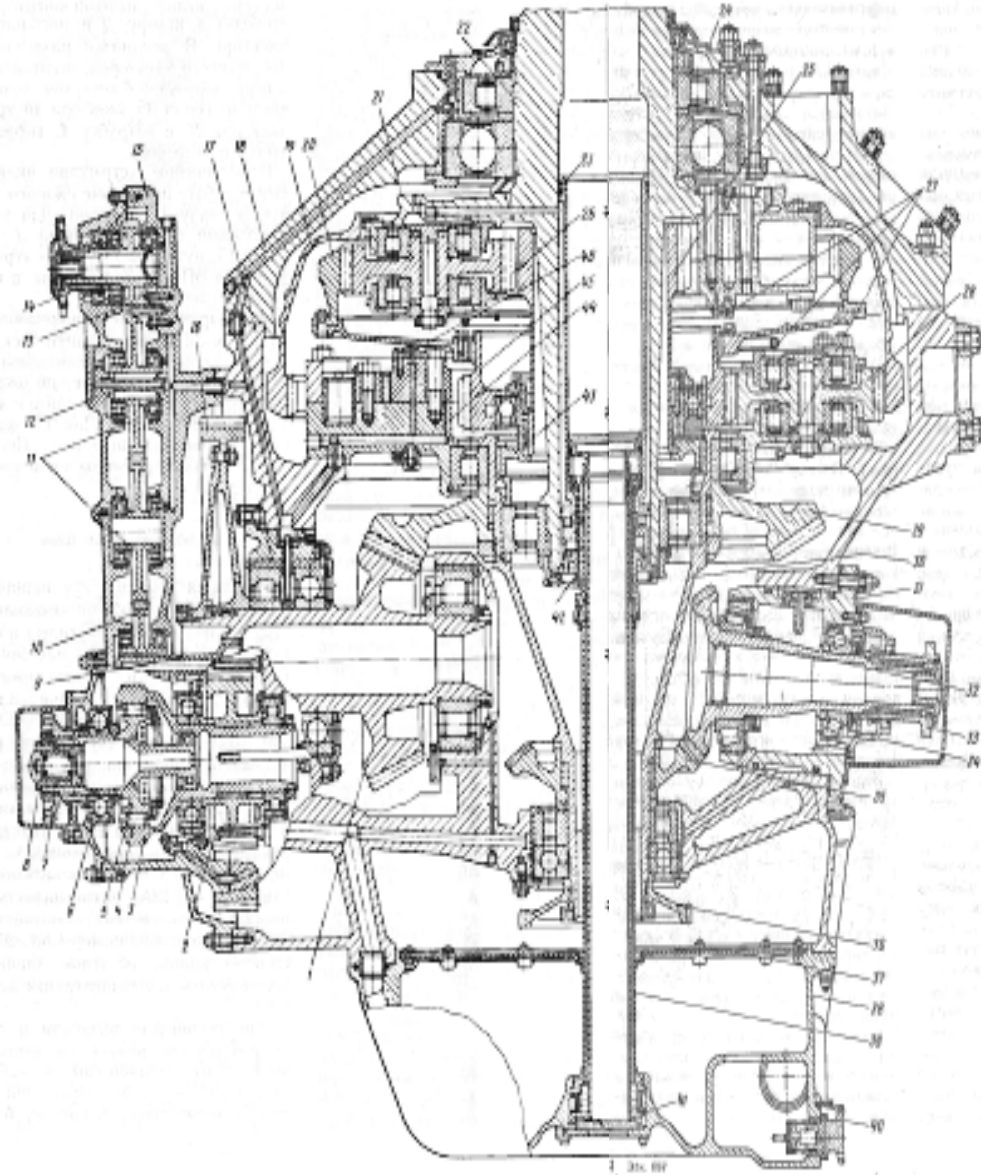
Поздовжній розріз головного редуктора ВР-8А:
